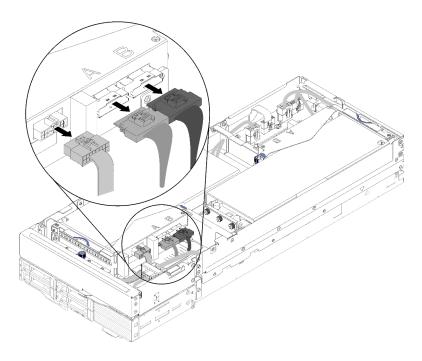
Desconectando o PCIe#3-A, PCIe#4-B e o cabo diverso da placa riser
